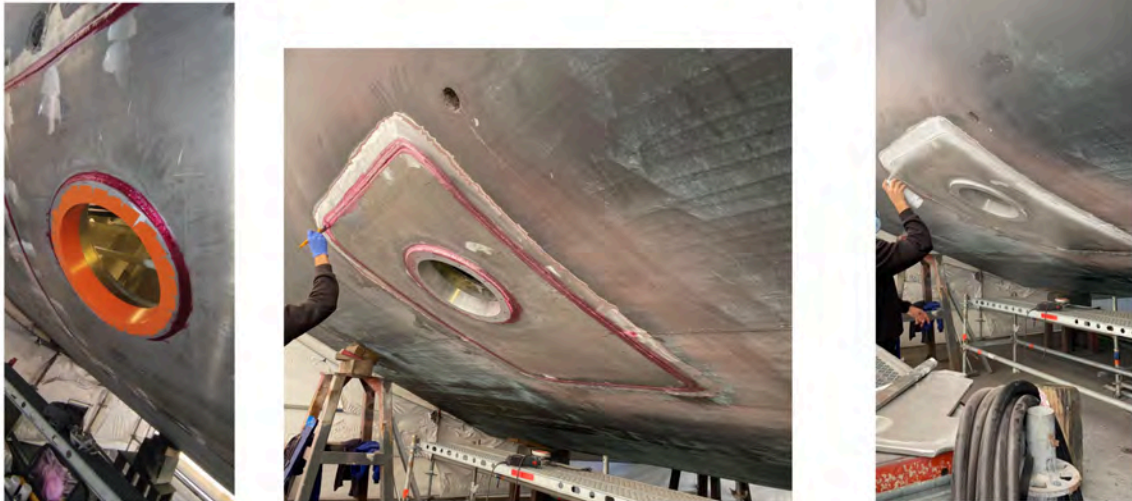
END en soldadura (Fuente: Trabajo de campo)
